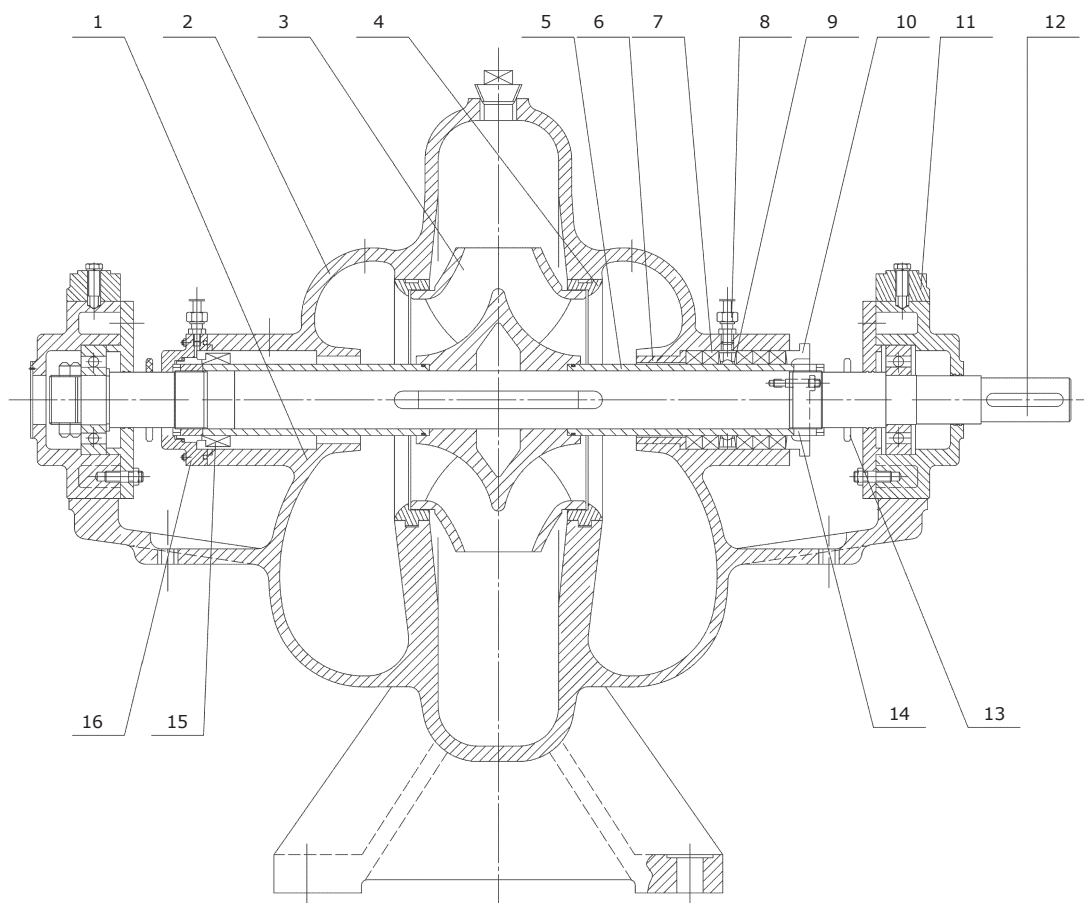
Вид в разрезе, стандартный тип исполнения 2
